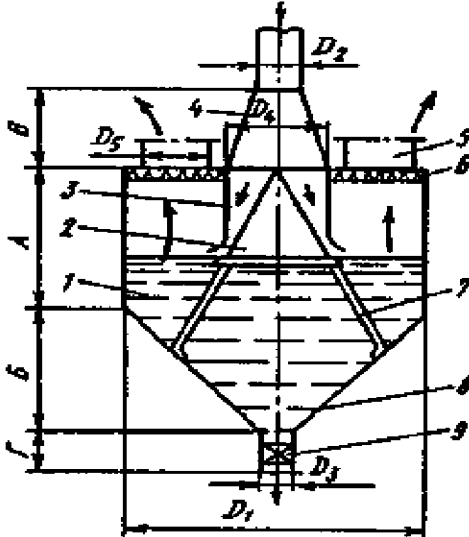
Мокрый пылеуловитель РИСИ: 1 - цилиндрическая камера; 2 - конус-рассекатель; 3 - отражатель; 4 - диффузор; 5 - патрубок для отвода воздуха; 6 - каплеуловитель; 7 - лапки для крепления; 8 - бункер конической формы; 9 - патрубок для стока шлама.
